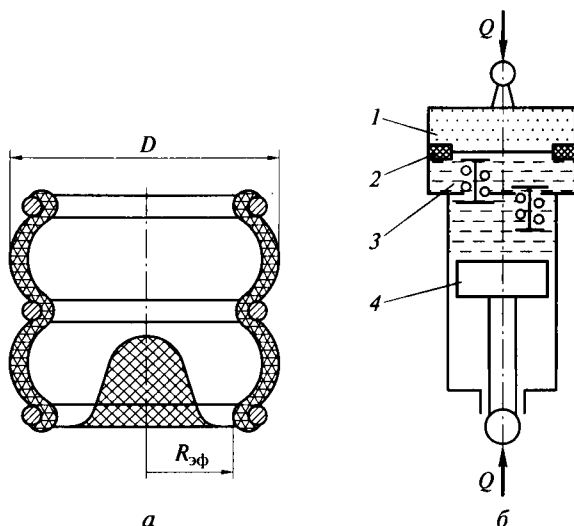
Баллон (а) упругого устройства пневматической подвески и цилиндр (б) гидропневматической подвески:
